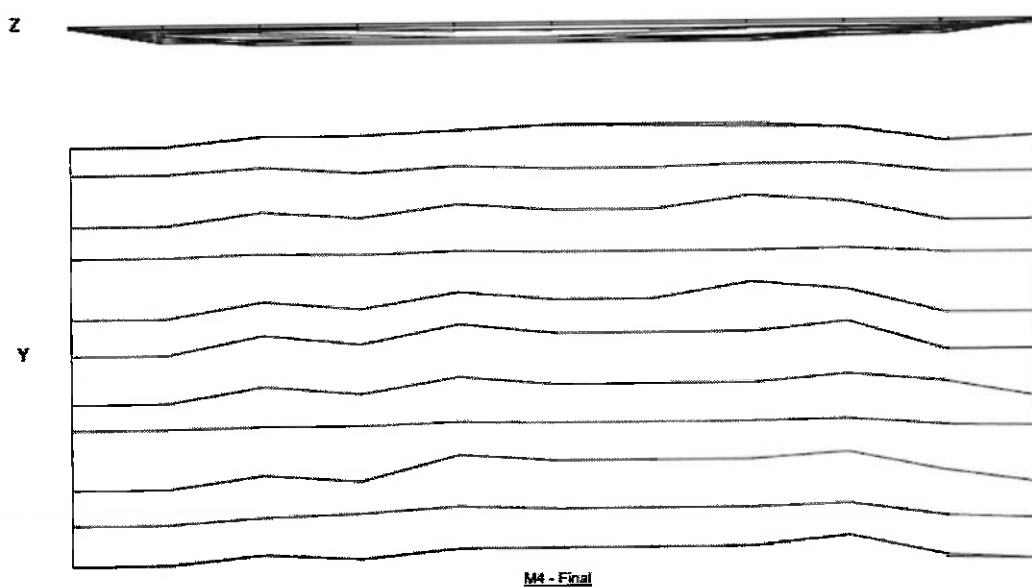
Ilustração da condição final da chapa com fator de escala após a segunda soldagem para a mesa 4.
